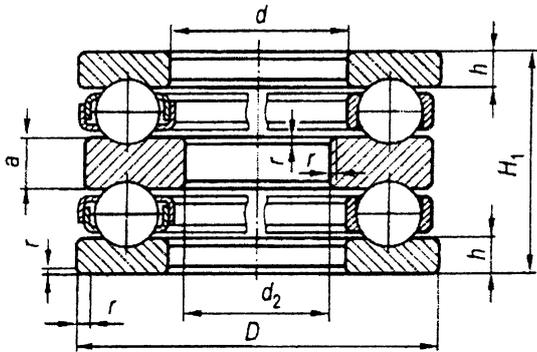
Подшипник шариковый упорный двойной исполнения 38000H
